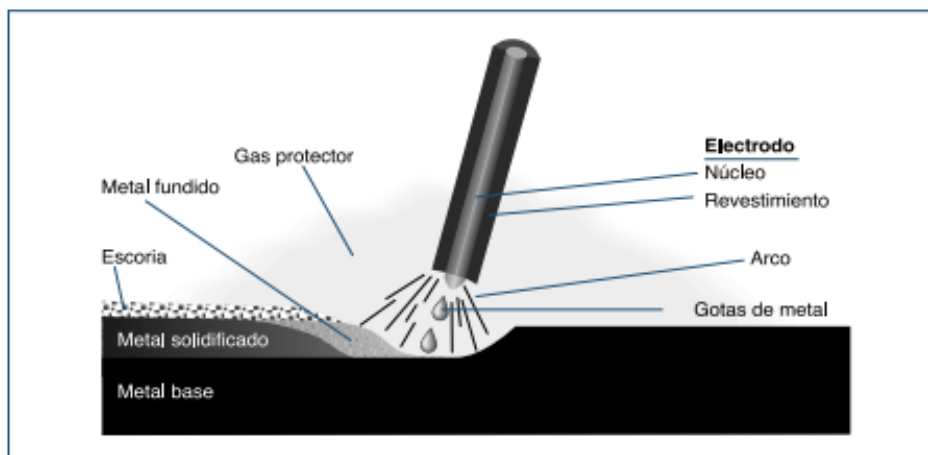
Soldadura por arco de metal protegido (SMAW) [23].
